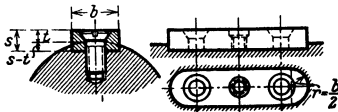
Gewinde in der Mitte für Abdrückschraube.
